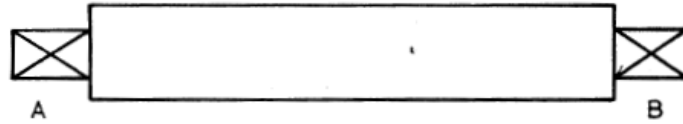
Eje rotatorio montado sobre cojinetes.
